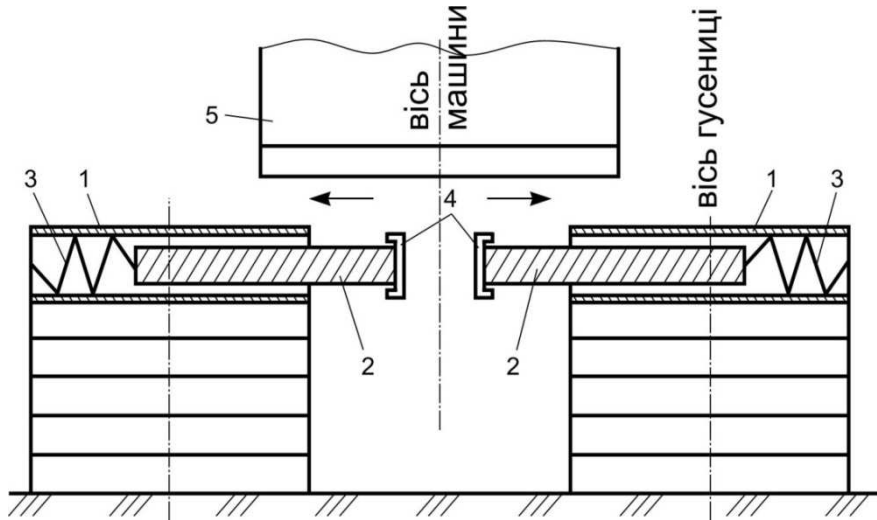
Конструктивна схема гусеничного ходового обладнання:
